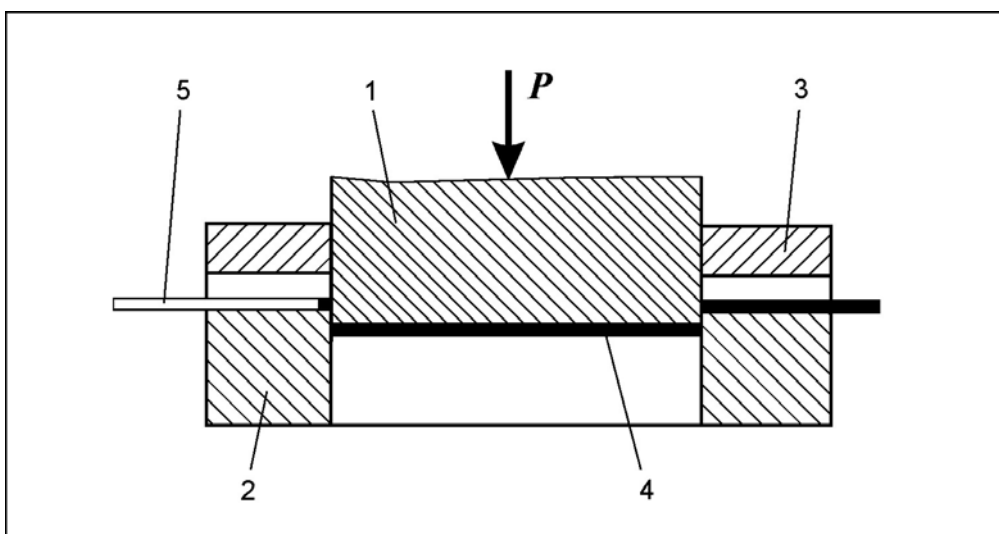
Схема операції вирубання: 1 – вирубний пуансон; вирубна матриця; 3 – жорсткий знімач; 4 – деталь (заготовка), що вирубана; 5 – штаба (стрічка)
